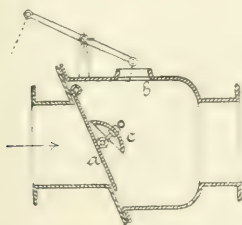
Rückschlagventil für Gebläsewindleitungen.
